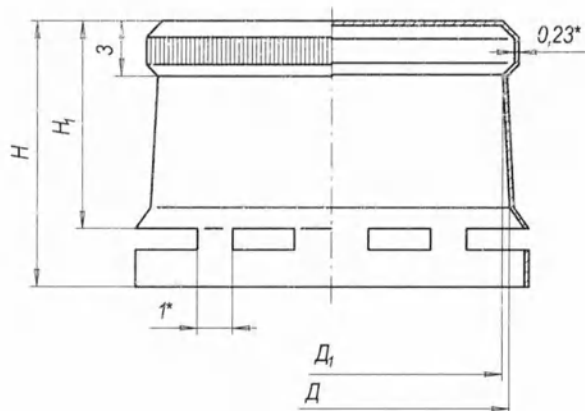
Конструкция, размеры алюминиевых колпачков с накатываемой резьбой и контролем первого вскрытия с уплотнительным элементом.
